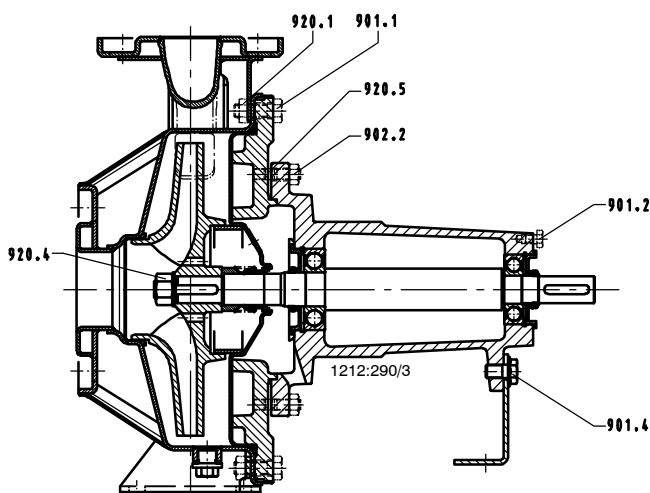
Места затяжки резьбовых соединений Etachrom NC с диаметром рабочего колеса 250, 50-200, 65-200, 80-200
